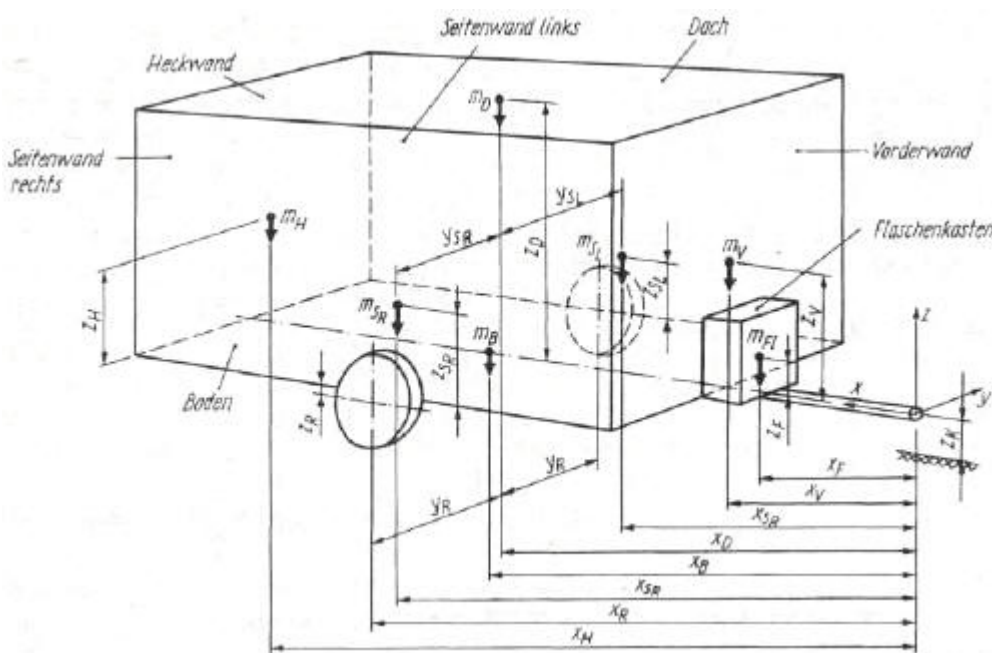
Belastungsschema des Aufbaues unter Beachtung aller zum Aufbau gehörenden Baugruppen
